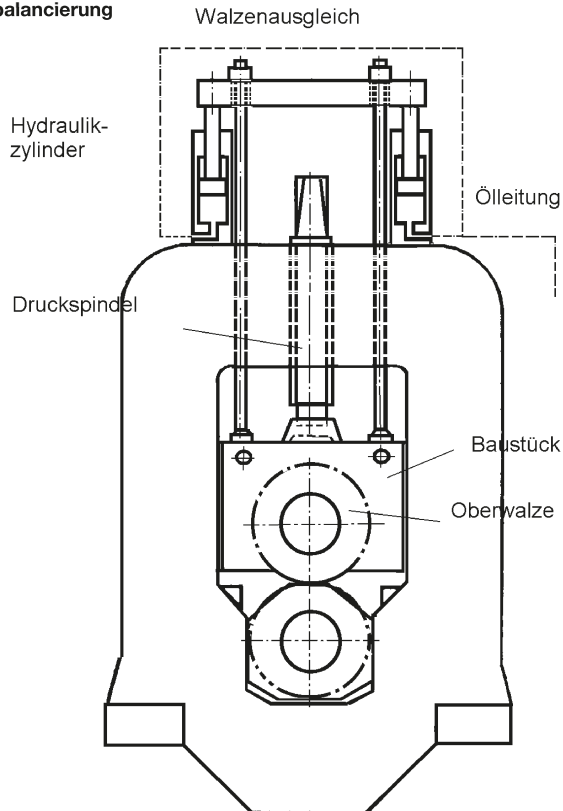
Walzenausgleich mit hydraulischem Gewichtsausgleich
